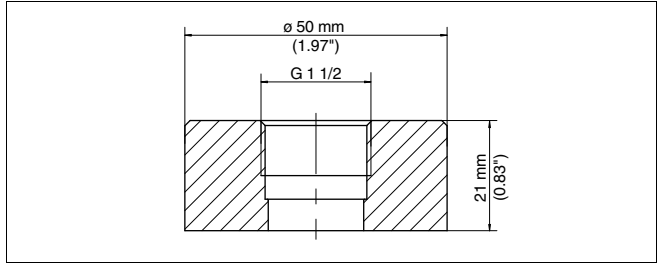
Maße Einschweißstutzen Gewinde G $\frac{1}{2}$  A nach EN 837
